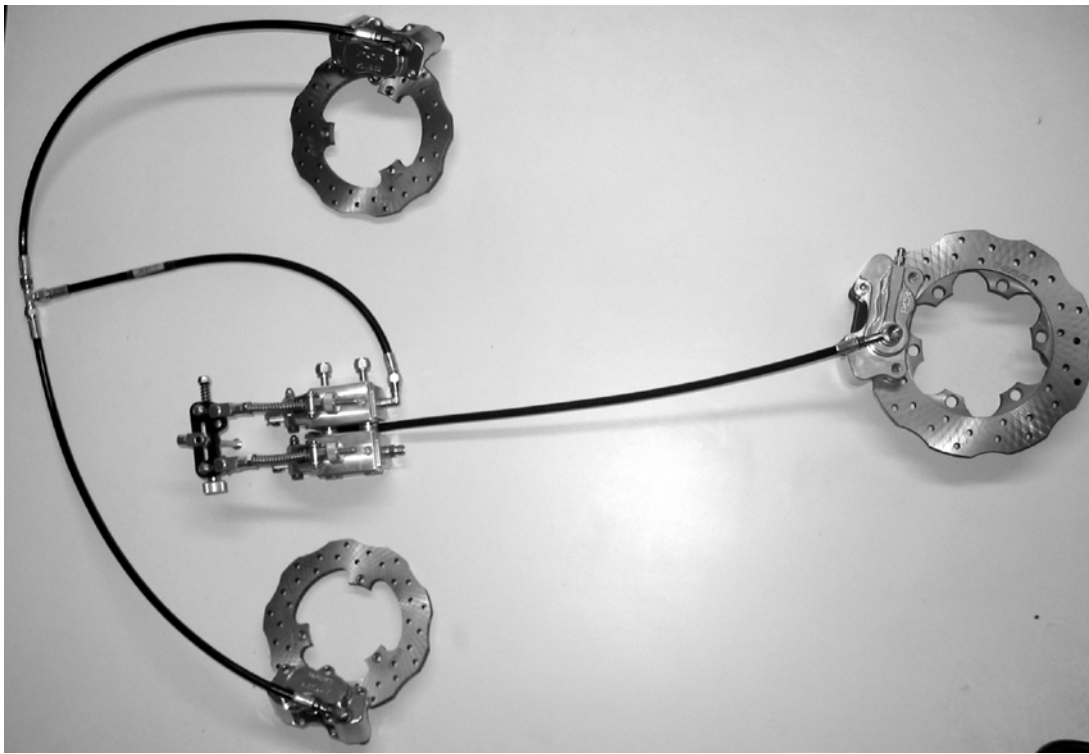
PHOTO VUE DE DESSUS DU SYSTÈME COMPLET ASSEMBLÉ
